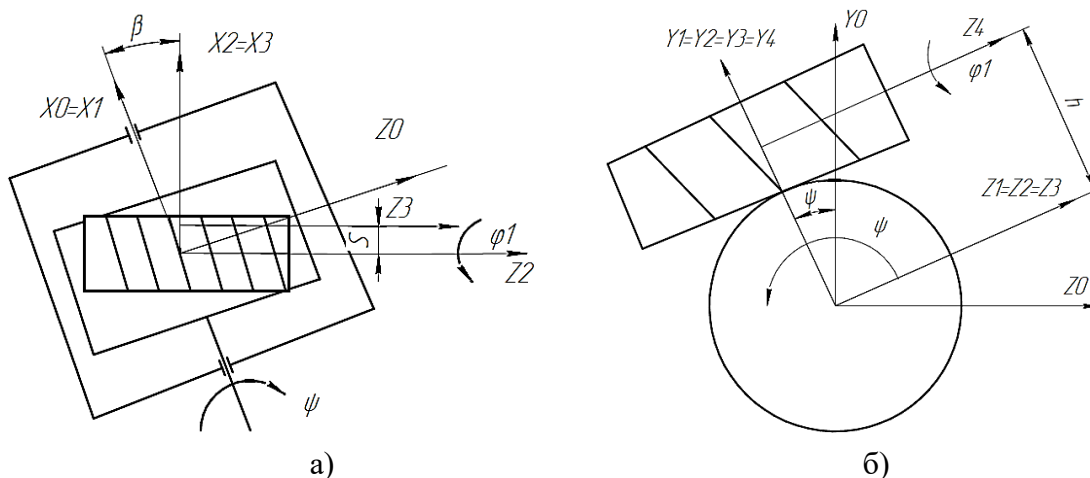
Схема взаємодії оброблюваної деталі і інструмента: а) вид зверху та б) вид збоку
